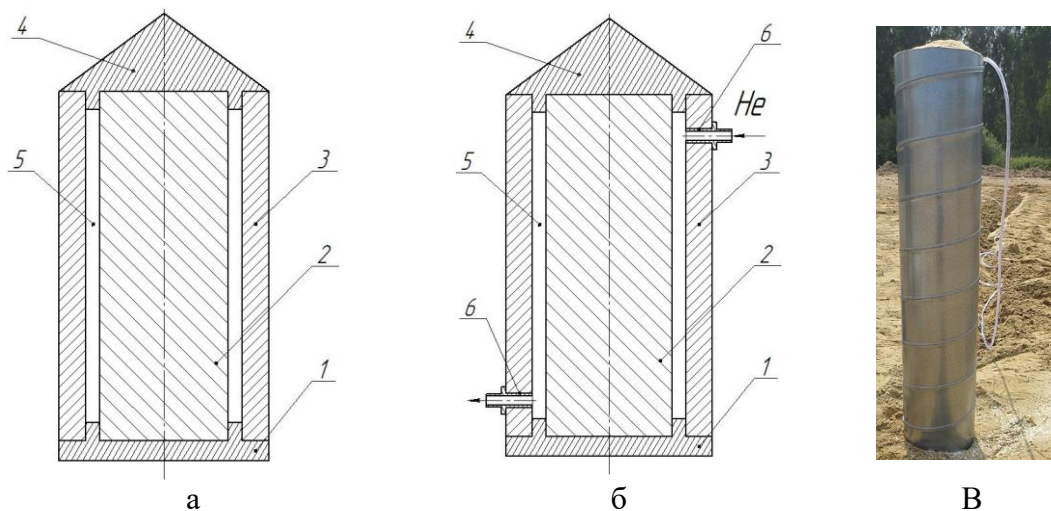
Схемы сборок исходных элементов под сварку взрывом: а – схема с использованием воздуха; б – схема с использованием гелия; в – сборка на полигоне
